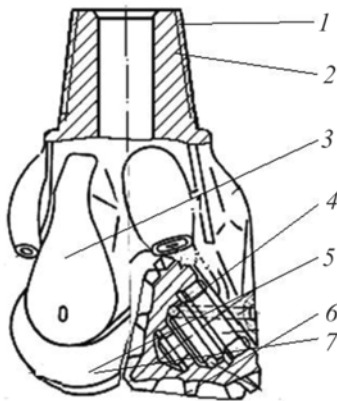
Виды аварий с долотами: 1 – самопроизвольный отворот резьбового соединения; 2 – слом по телу резьбового соединения; 3 – слом лапы долота; 4 – разрушение подшипников; 5 – разрушение тела шарошки; 6 – разрушение, скалывание вооружения шарошки; 7 – заклинивание шарошек, оставление шарошек
